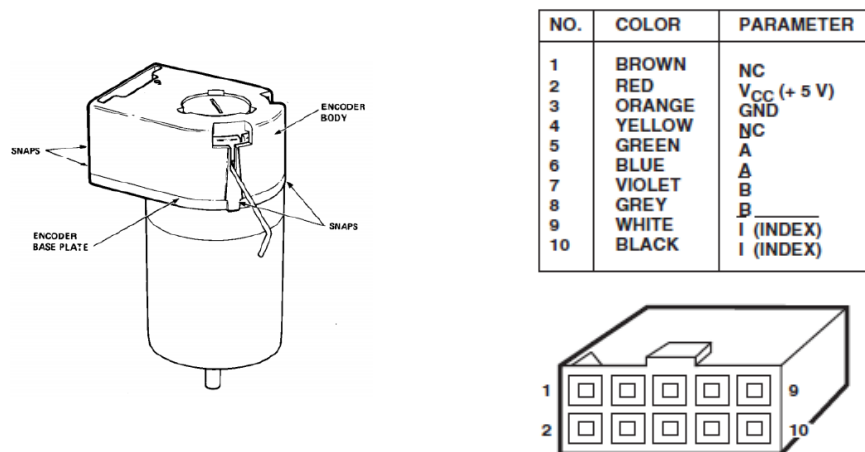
A la izquierda, motor+encoder, a la derecha, esquema de conexiones
